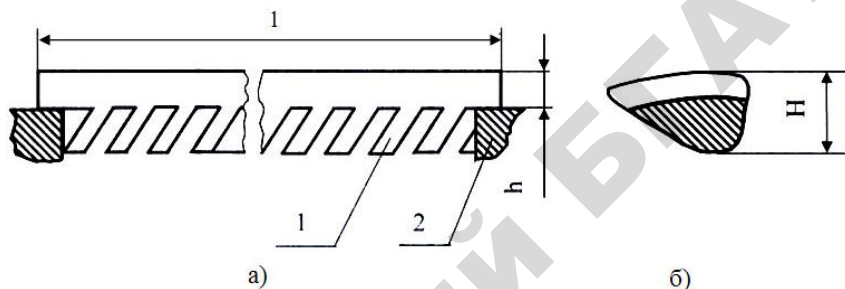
Схема установки разрыхлителя на корпус рабочей камеры
